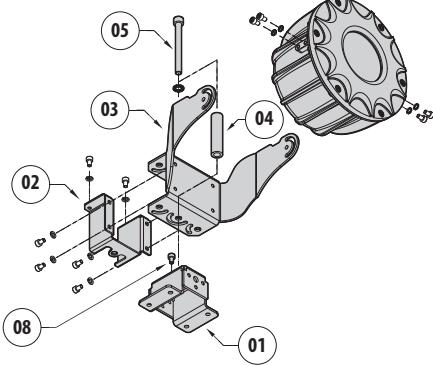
Geländerbefestigung mit Kableingang nach oben.
